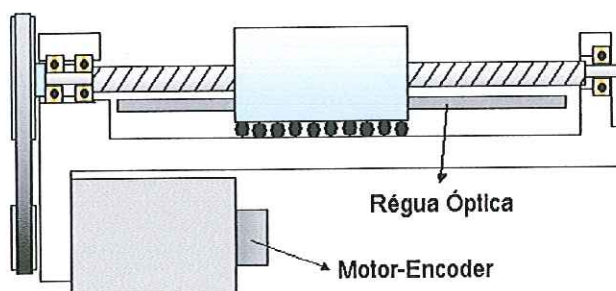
Configuração padrão de transmissão de movimento para o carro [FONTE: MODERN MACHINE SHOP ONLINE SUPLEMEN]
